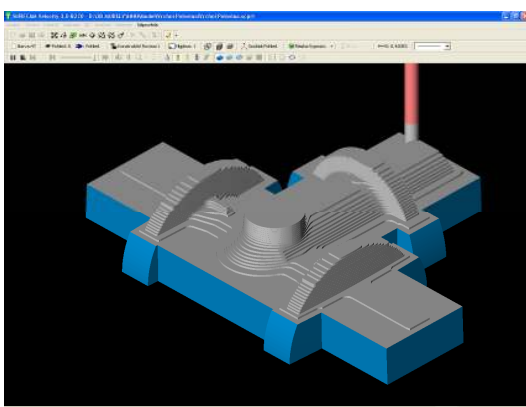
Načtení polotovaru ve formátu.STL Obr. 4.11 Volba barvy hladiny nástroje
